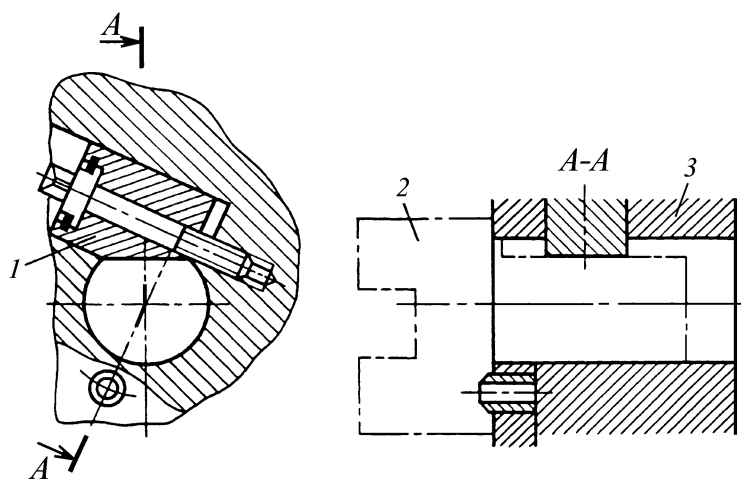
Закрепление резцедержателя в револьверной головке
